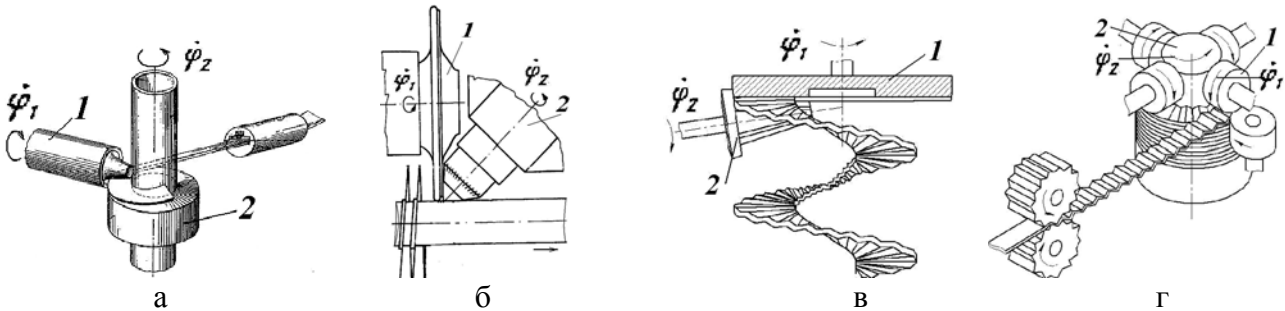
Схеми формоутворення ГЗ за допомогою інструментів з робочими поверхнями у вигляді конусних та плоских поверхонь:
